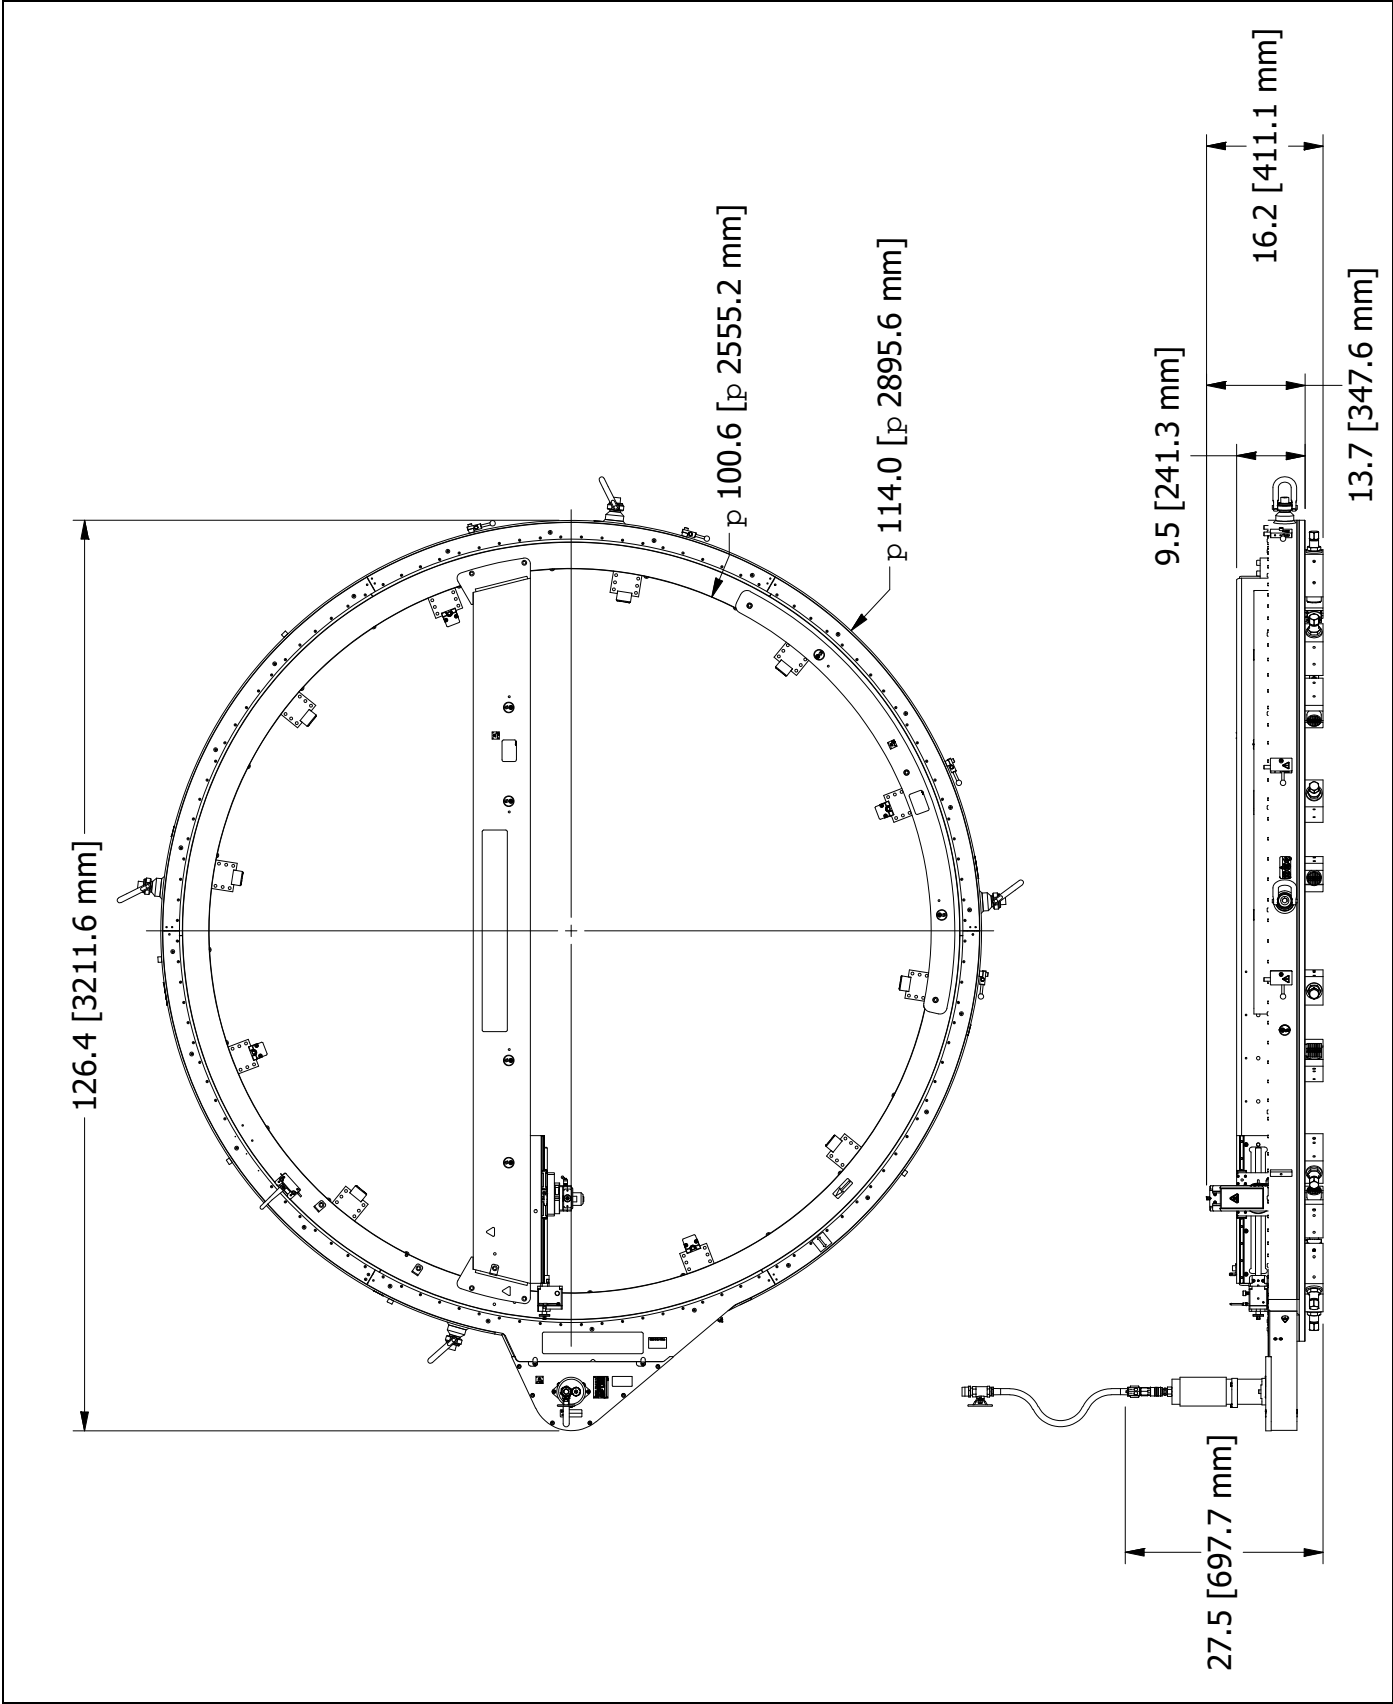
DIMENSIONES DE ODF100 SPEED FACER (N/P 94790)
